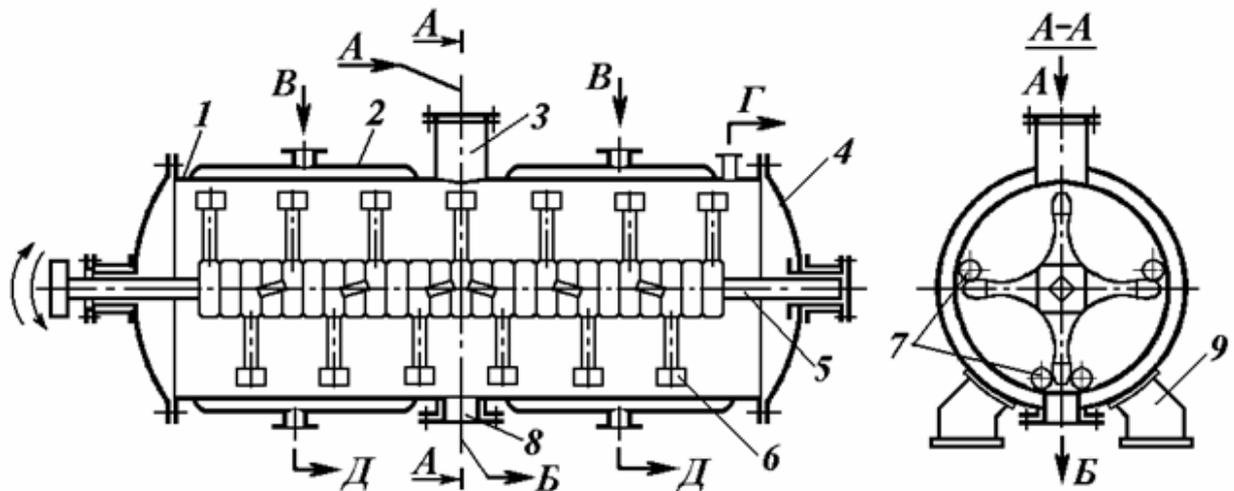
Гребкова вакуум-сушарка: 1 - корпус; 2 - парова сорочка; 3 - люк завантажувальний; 4 - кришка; 5 - вал; 6 - гребки; 7 - труби-качалки; 8 - люк для вивантаження; 9 - опора; Потoki: А - вологий матеріал; Б - висушений матеріал; В - пара насичена; Г - пара вологи; Д - конденсат водяної пари.
